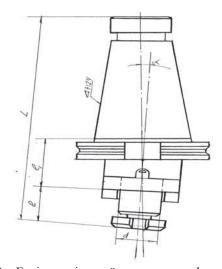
Ескіз спеціальної оправки для фрези-протяжки
